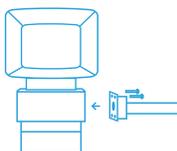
Instale o conjunto de flange no corpo da válvula V2X.
